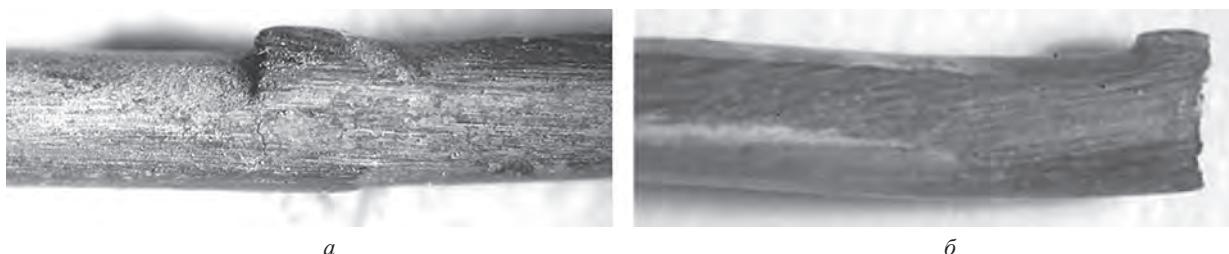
Внешний вид сварного шва на проволоке с дефектом «несоосность» (а) и вид обрыва проволоки (б) по причине несоосности сварного соединения
